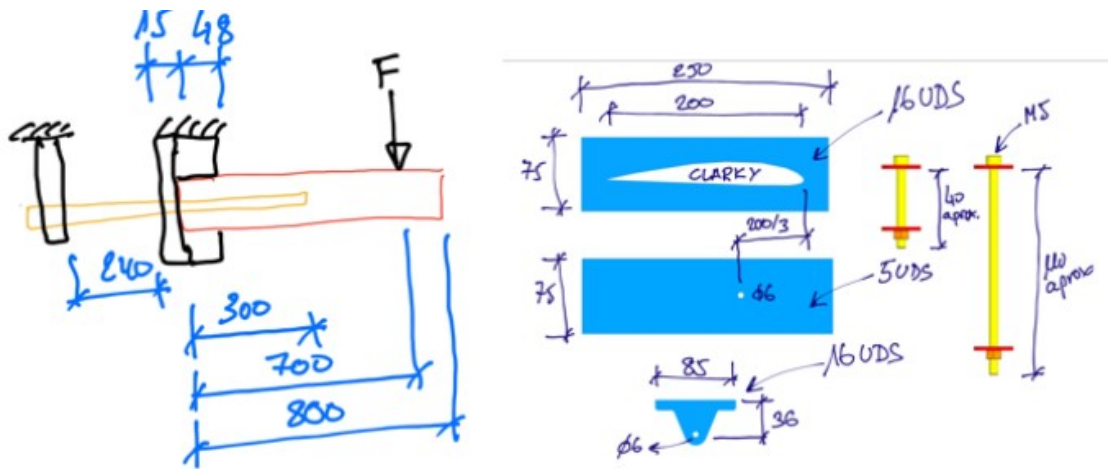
Detalle constructivo del utillaje de amarre (2/2)
